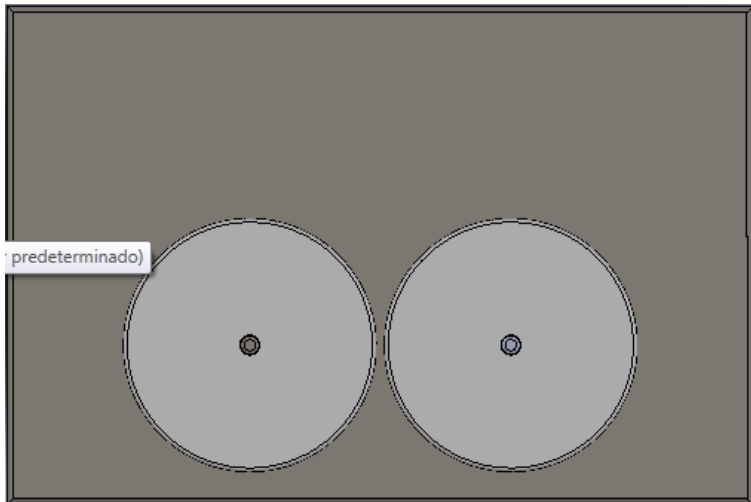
Vista frontal do modelo de máquina de lapidar Faceting Head CNC (Elaborado pela Equipe do Projeto)
